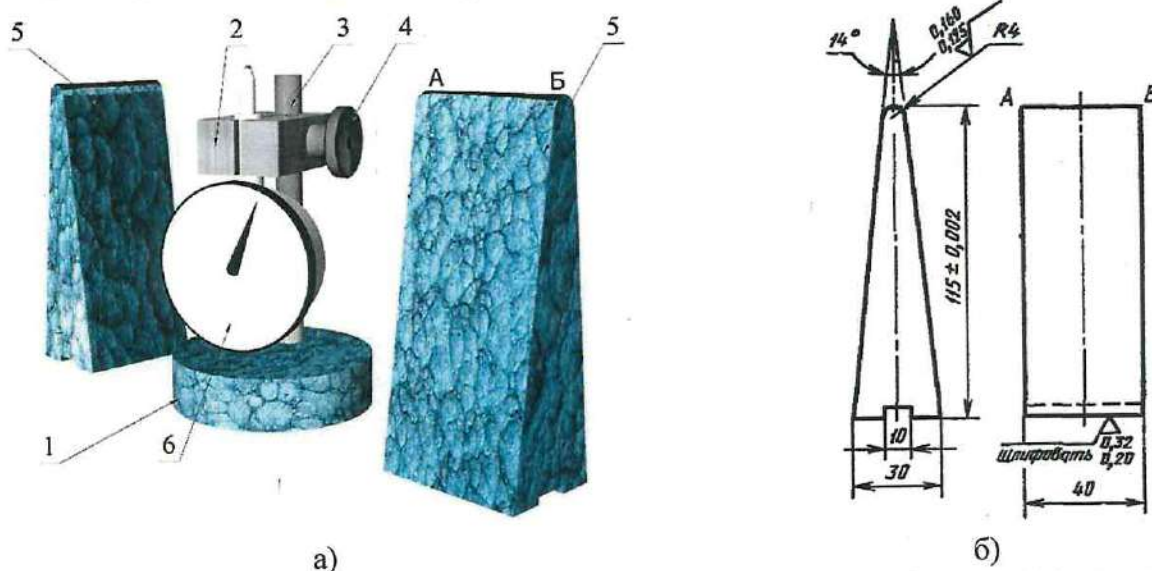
Приспособление для измерения отклонения от плоскостности методом сличения с поверочными линейками: а) – общий вид приспособления; б) – опорная призма
